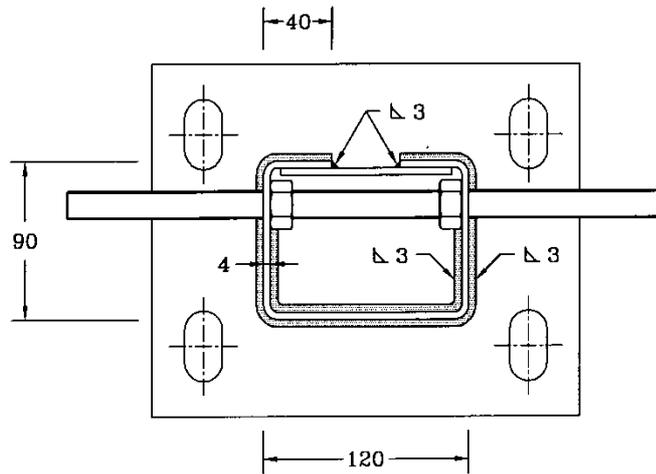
DETAIL DES PIÈCES D'ANCRAGE
